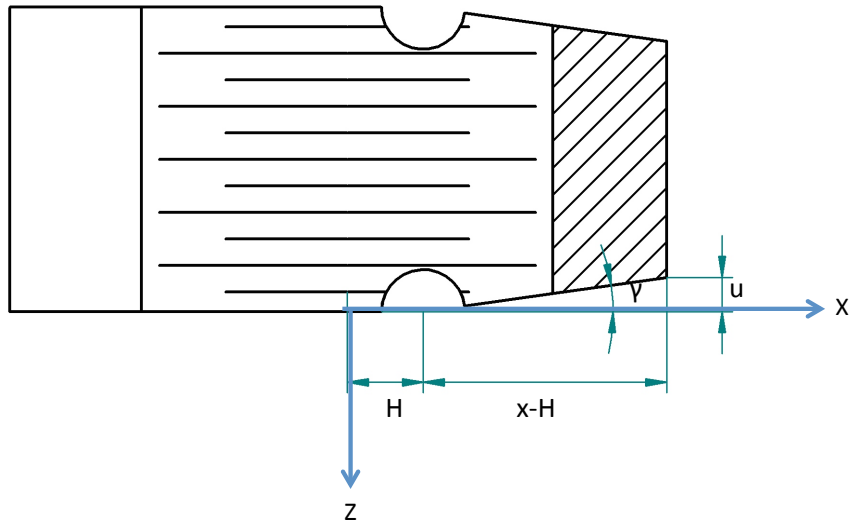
Plano XY. Vista superior, triángulo formado por el rebaje
